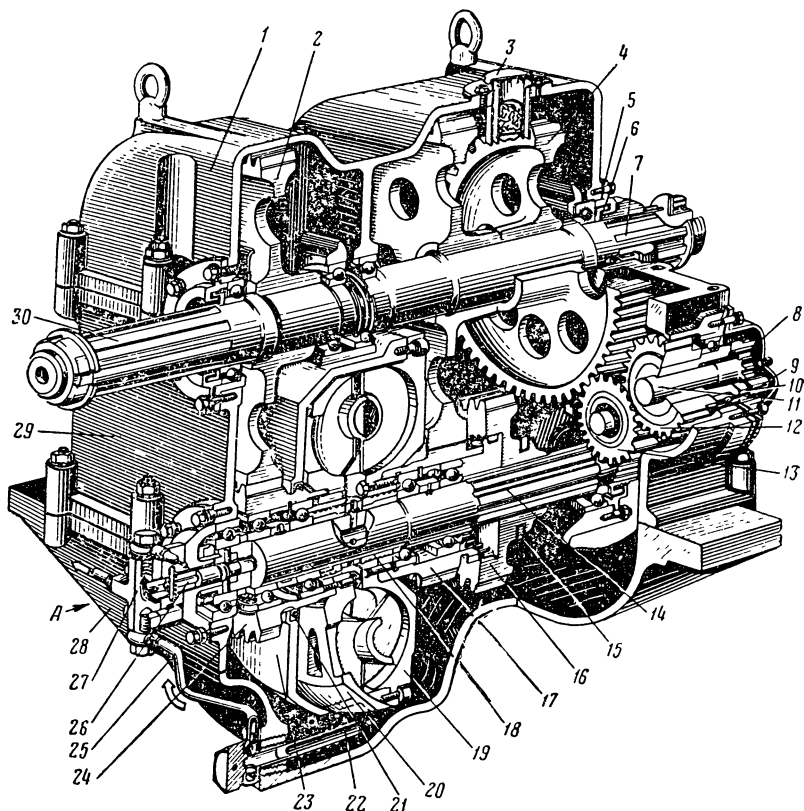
Гидромеханический редуктор с алюминиевыми колесами гидромуфты:
